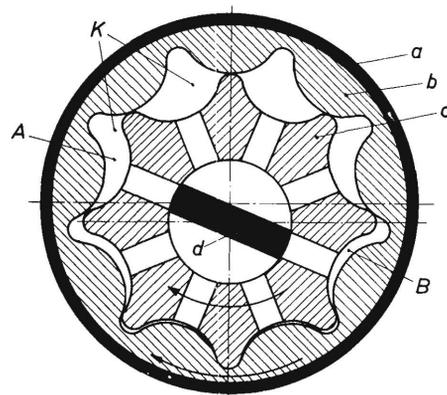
Schema einer exzentrischen Zwillingläufer-Drehkolbenmaschine.
